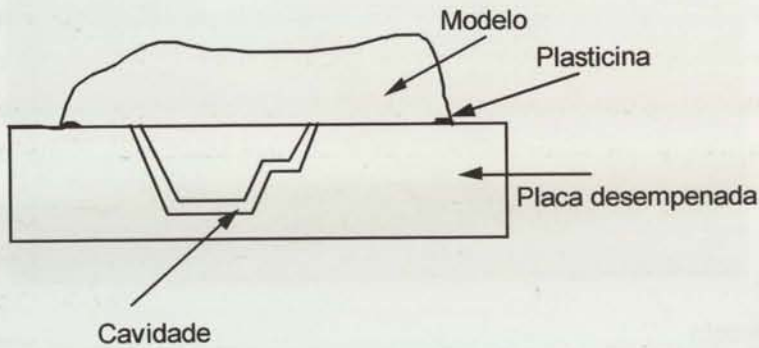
Cavidades com plano de apartação plano (Alves, 1999).
